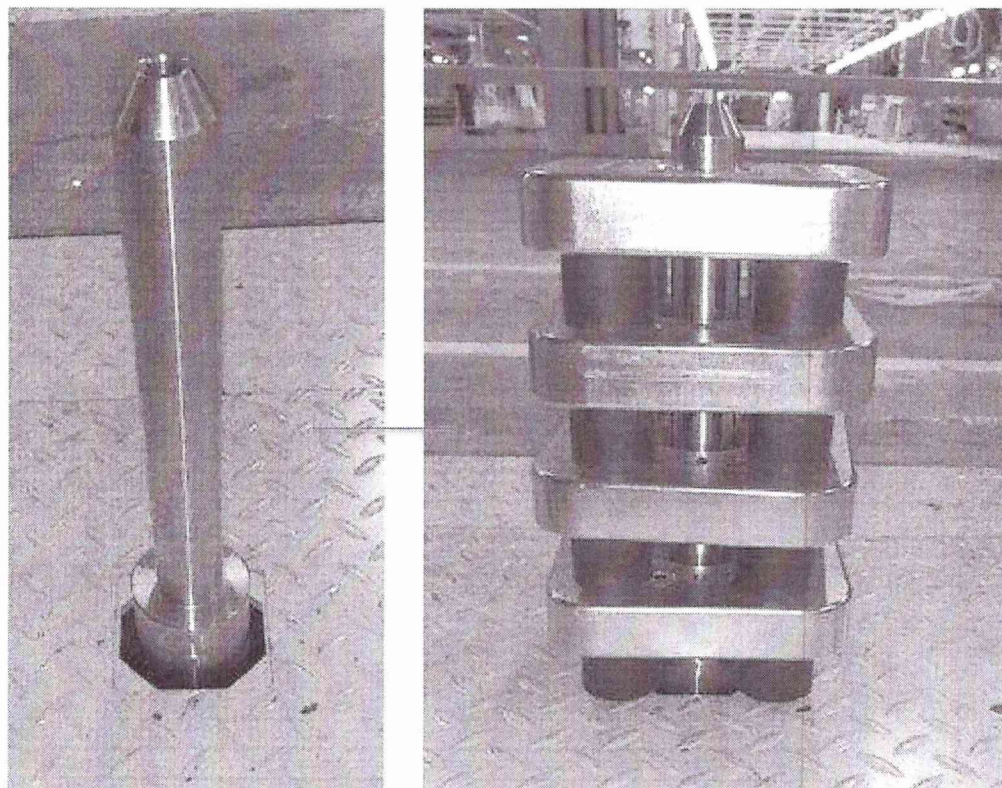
Установка цилиндрической опоры и калибровочных грузов
